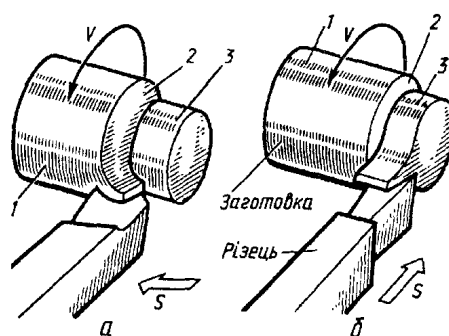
Рухи у процесі токарної обробки та поверхні на оброблюваній заготовці: а - робота підрізним різцем; б - відрізним; V - головний рух; S - рух подачі; 1 - оброблювана поверхня; 2 - поверхня різання; 3 - оброблена поверхня
